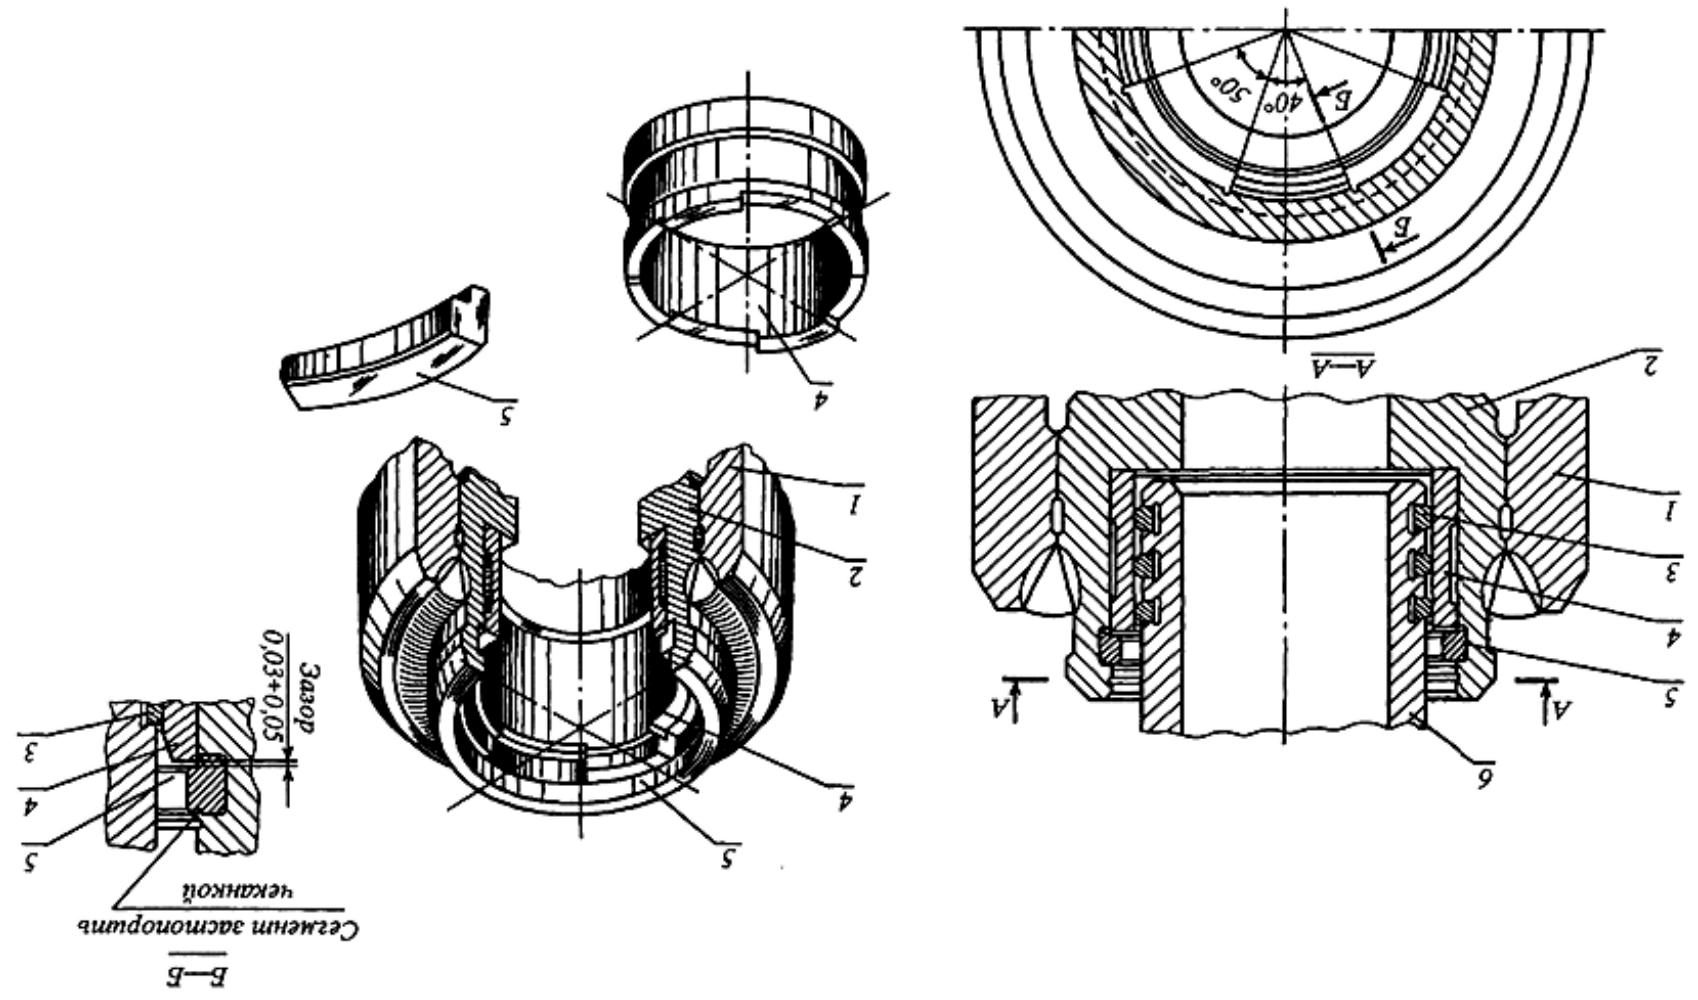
Поршневое соединение патрубков внутреннего и наружного корпусов цилиндра: 1 – корпус внутреннего цилиндра; 2 – паровпускной патрубок сопловой коробки; 3 – поршневое кольцо; 4 – втулка; 5 – стопорный сегмент; 6 – паровпускной штуцер
